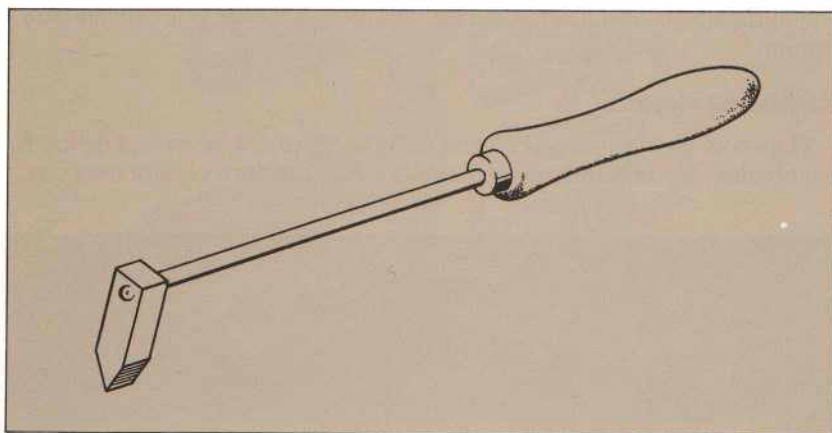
Ejecución de la soldadura dura por bloque.
